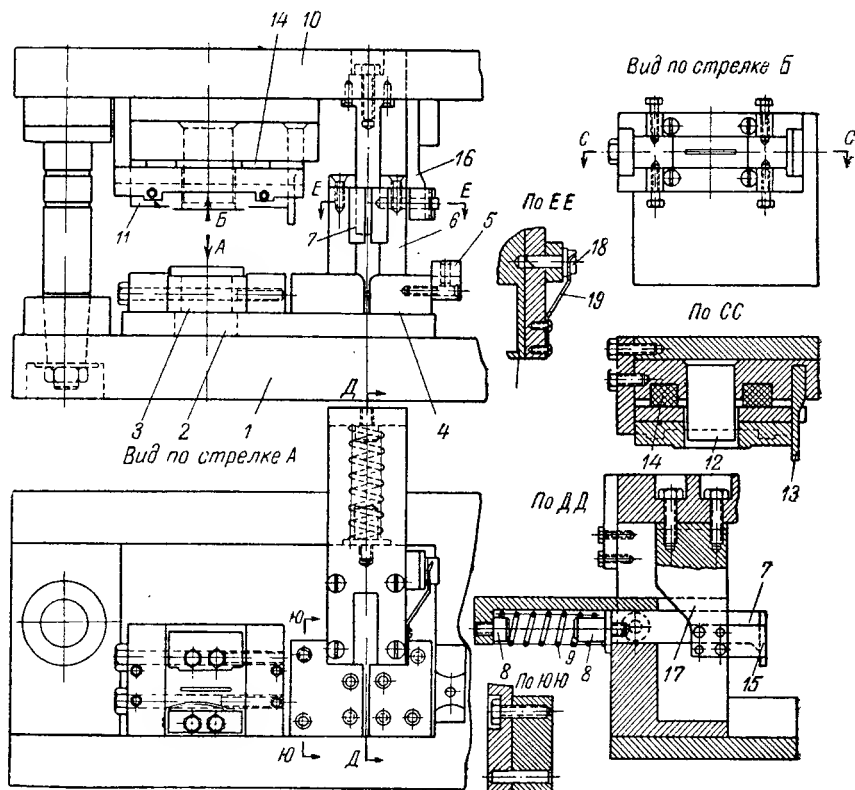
Конструкция штампа-полуавтомата для вырубки и гибки петушков
